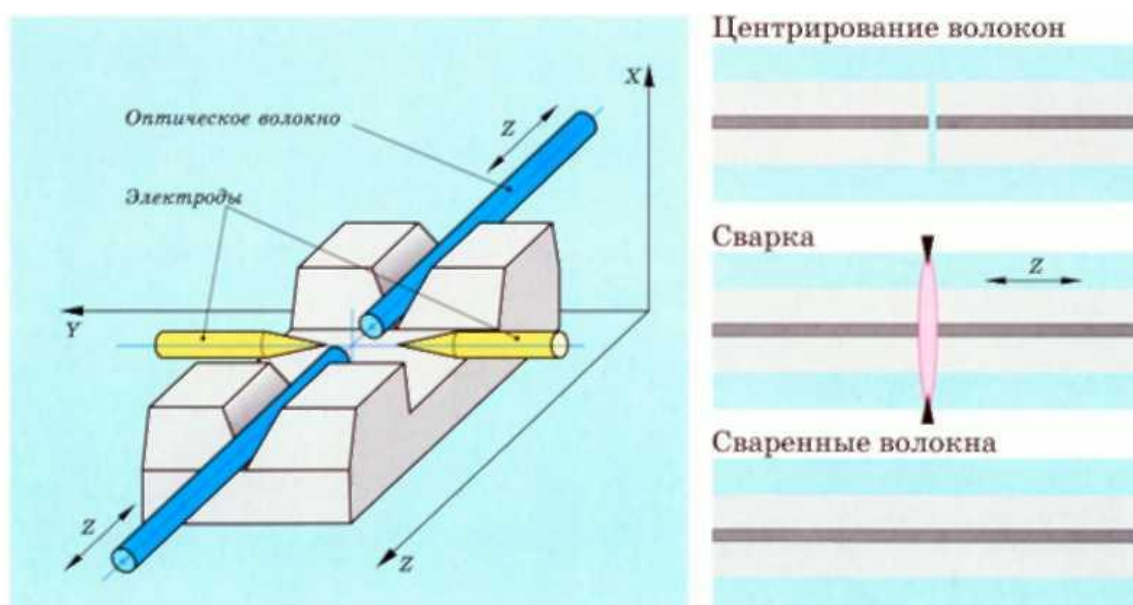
Принцип работы сварочного аппарата Fujikura FSM-18S
